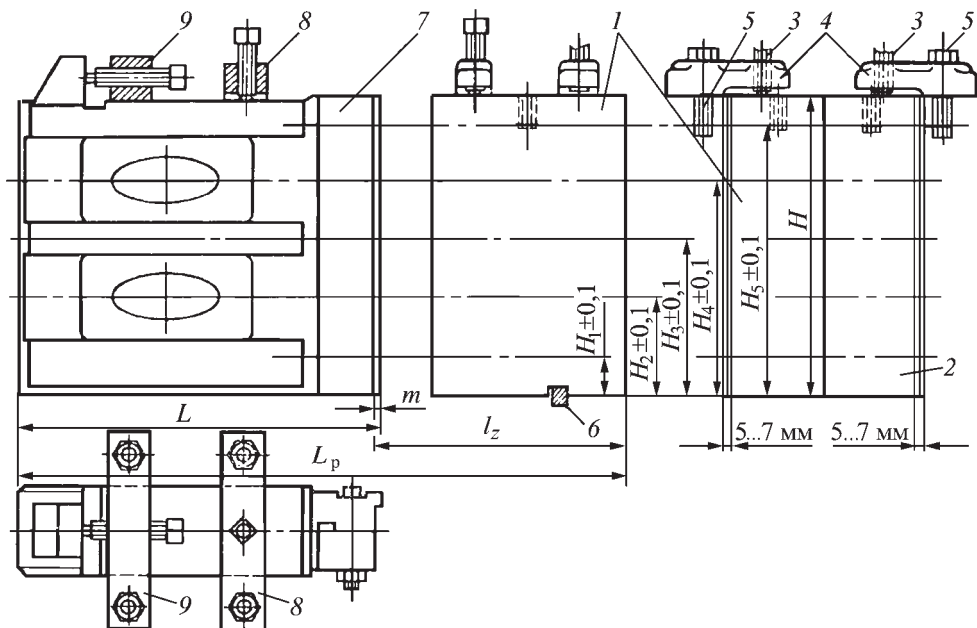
Схема крепления и габаритные размеры блоков штампов ГKM:
